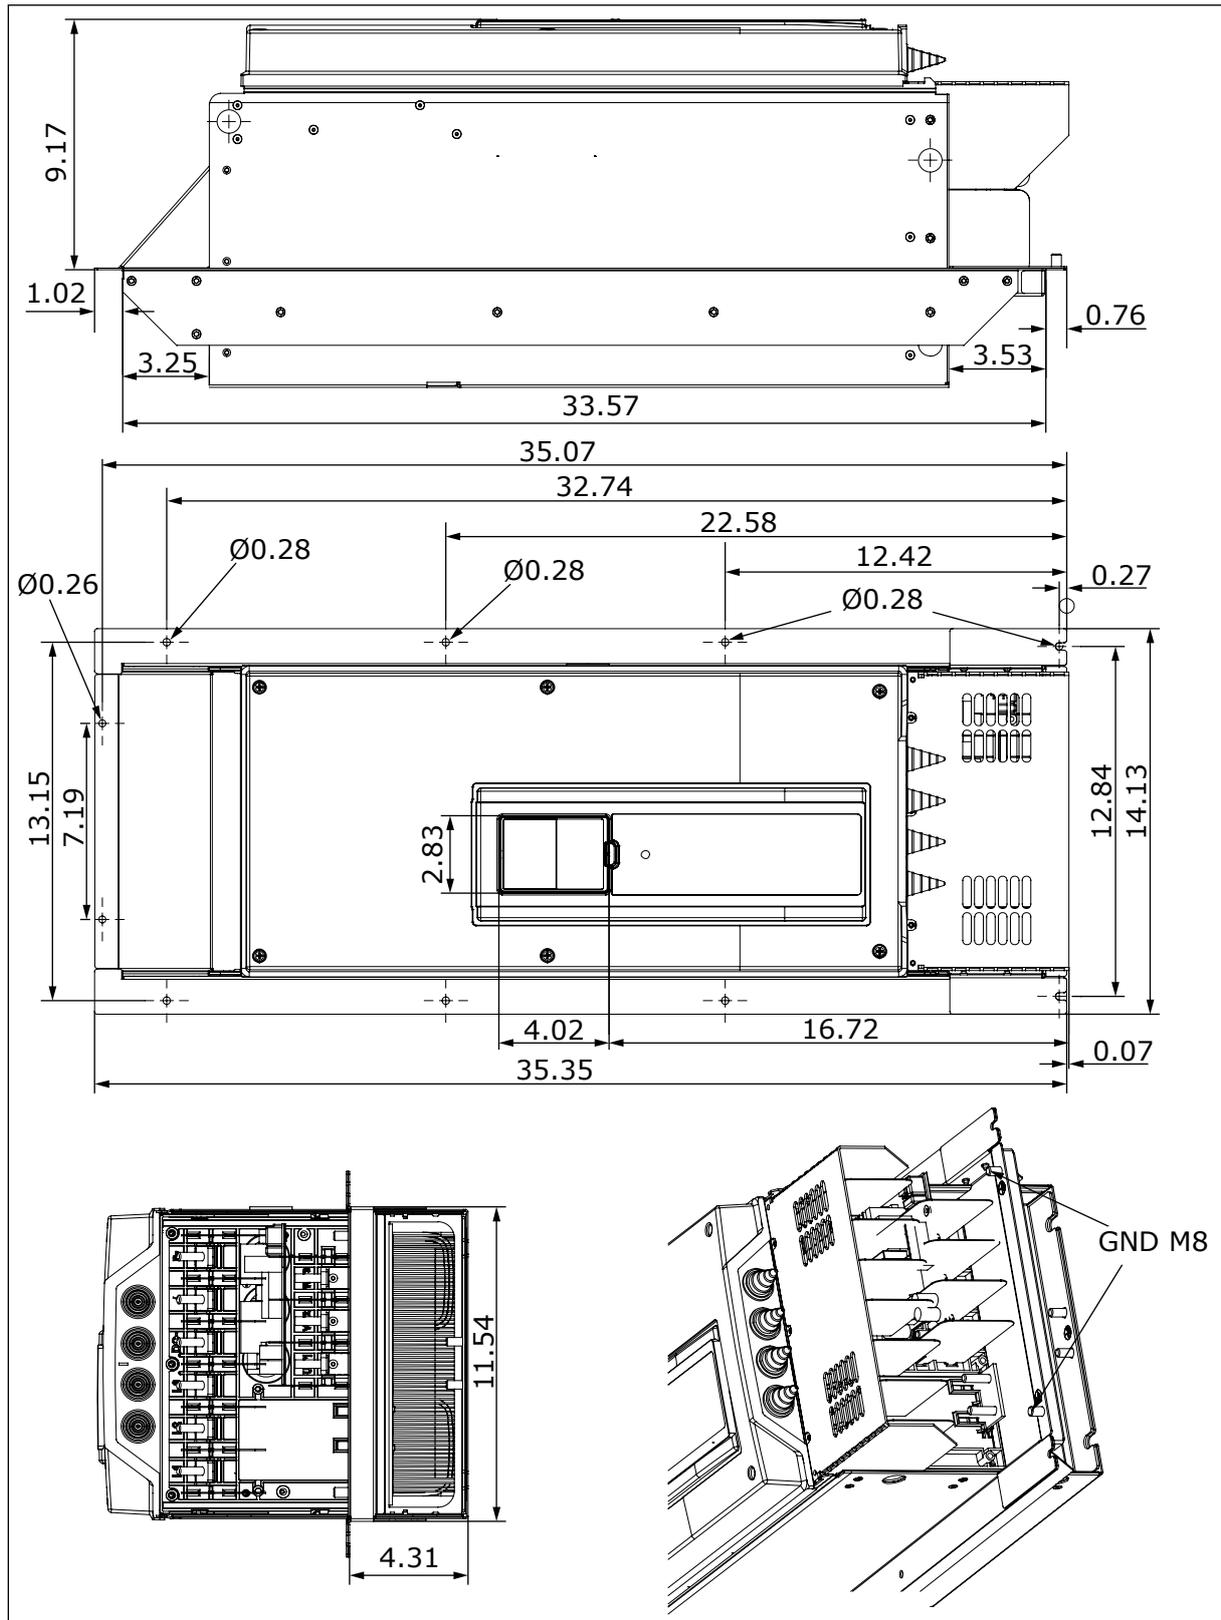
Abmessungen des Frequenzumrichters, Flanschbefestigung, MR8 [in]
